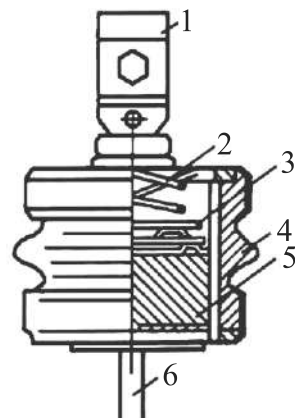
Конструкция разрядника для сетей напряжением 0,38 кВ: 1, 6 – зажимы; 2 – пружина; 3 – искровой промежуток; 4 – фарфоровый корпус; 5 – вилитовый диск
